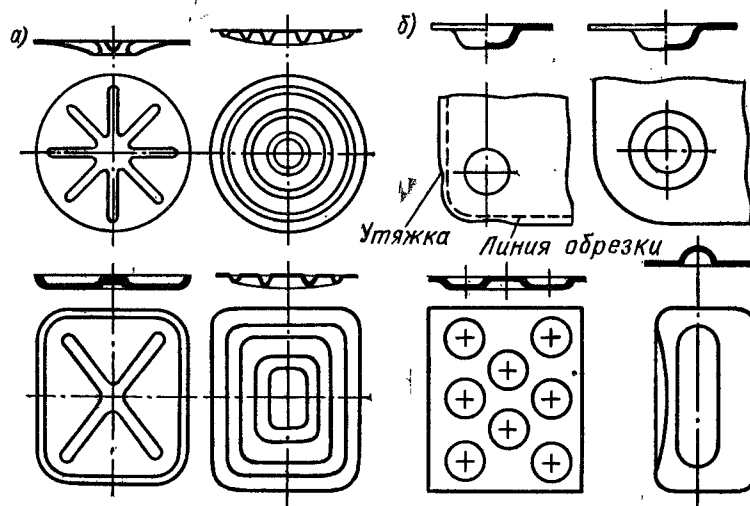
Примеры рельефной формовки: а — штамповка ребер жесткости; б — штамповка выдавок
